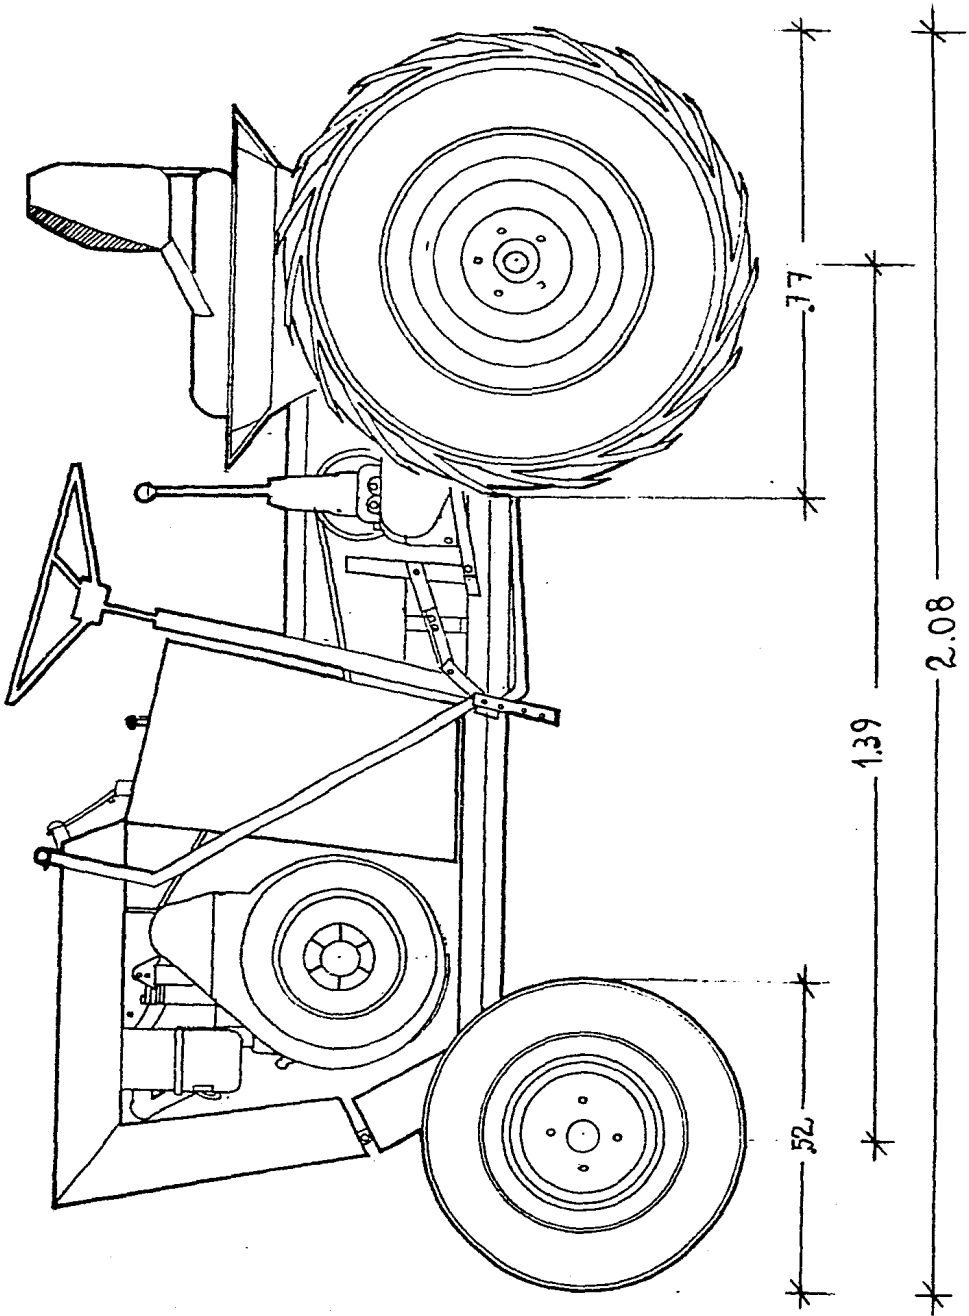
Dimensiones del minitractor. Vista lateral. (m)
